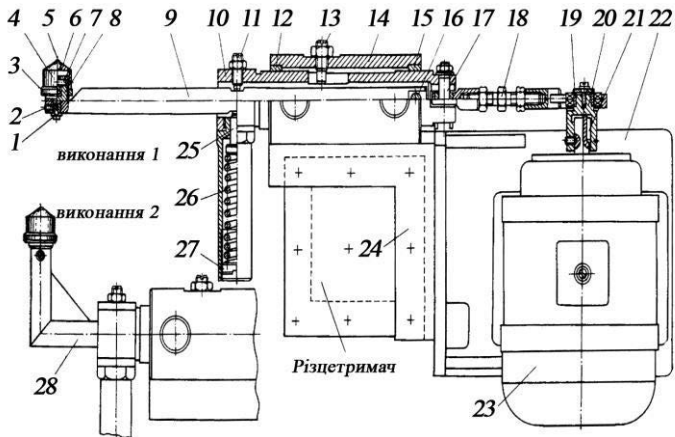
Універсальний пристрій для вібронакатування (вібровигладжування) деталей: 1 – гвинт; 2 – вісь; 3 – нарізне кільце; 4 – сепаратор-ковпачок; 5 – робоча кулька; 6 – вальниця кулькова; 7 – вісь; 8 – корпус; 9 – штанга; 10 – втулка; 11, 13 – гвинти обмежувачі; 12, 15 – вкладиші; 14, 20 – втулки; 16 – штифт; 17 – вісь; 18 – регульовальна гайка; 19 – ексцентрик; 21 – шпонка; 22 – основа; 23 – електродвигун; 24 – прямокутник; 25 – кінцевик; 26 – тарована пружина; 27 – нарізна пробка
